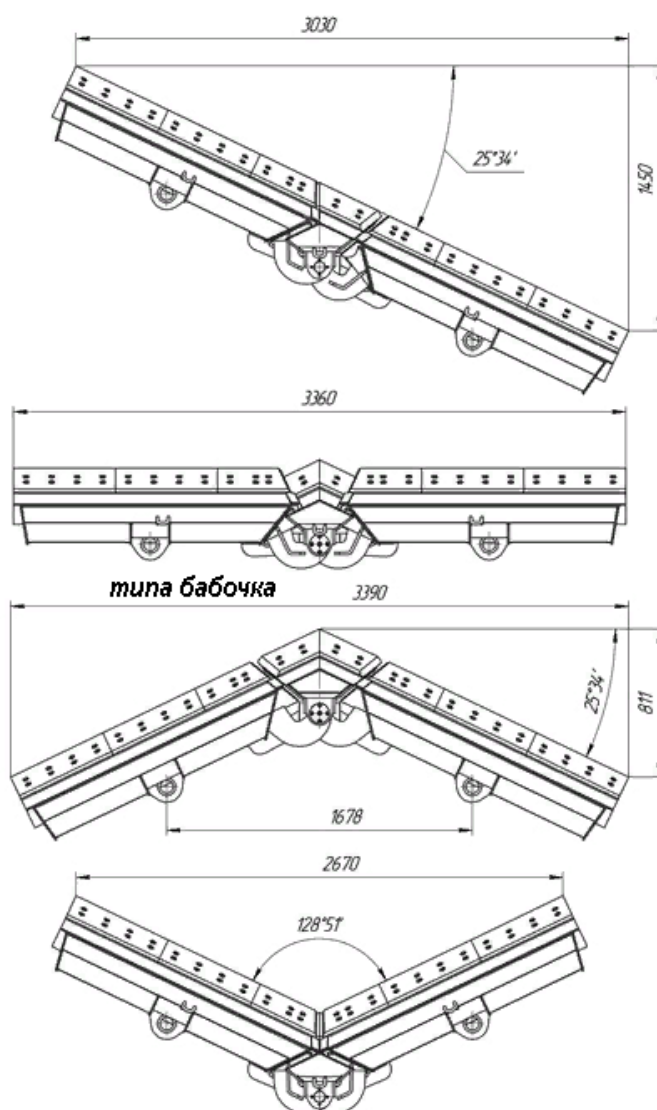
Схемы установки шарнирно-сочленённого отвала
